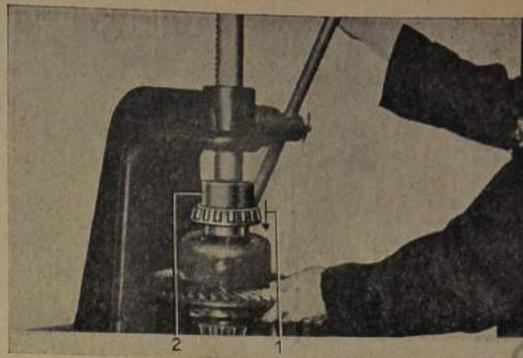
Kegelrollenlager auf Ausgleichgetriebe aufpressen
